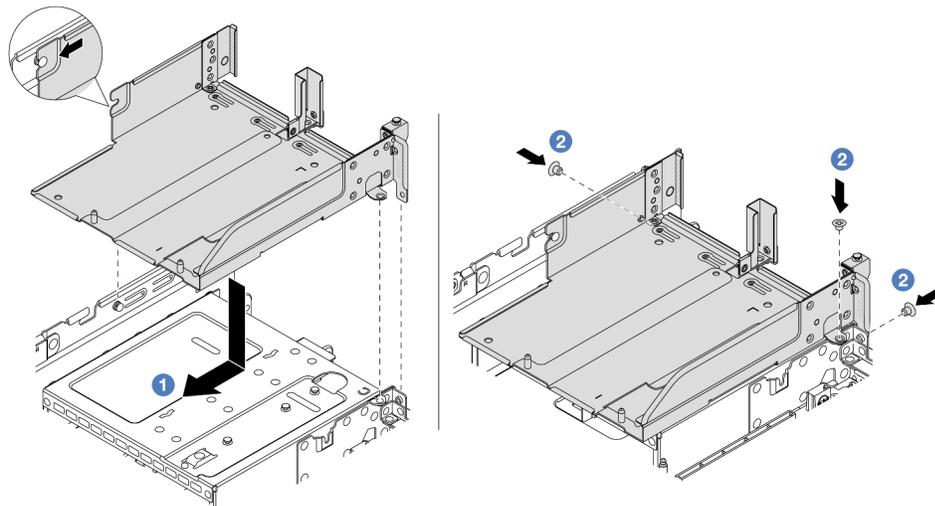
Installation d'un tiroir de boîtier de carte mezzanine
